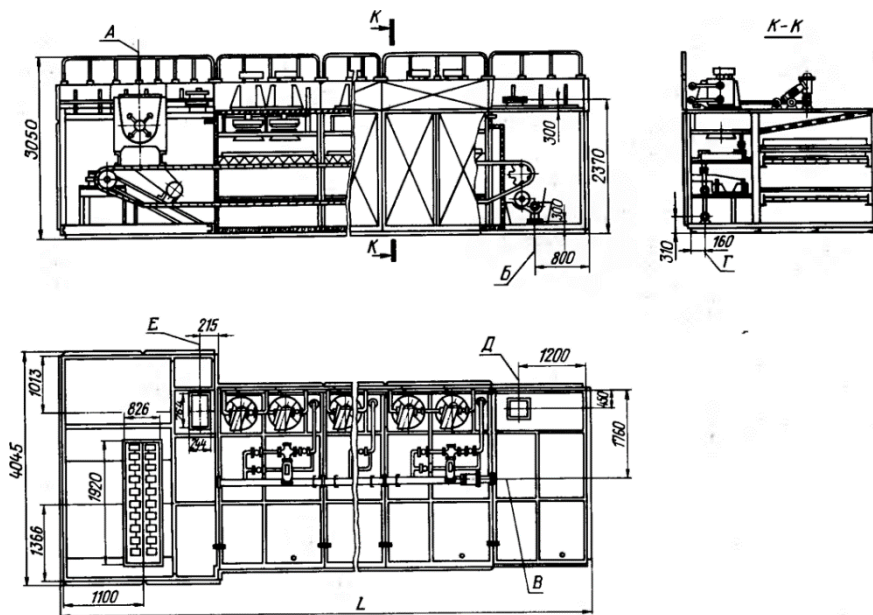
Стрічкова сушарка з формувальними вальцями
